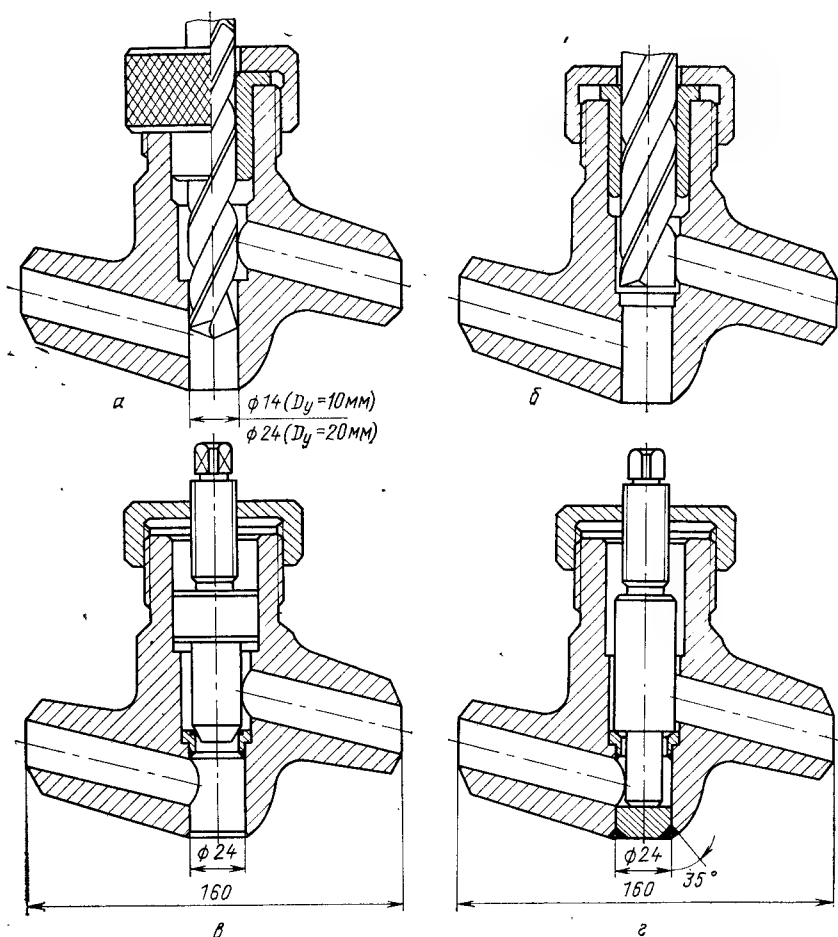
Схема обработки на сверлильном станке уплотнительной поверхности в корпусах вентилях $D_y = 10$ и 20 мм:
